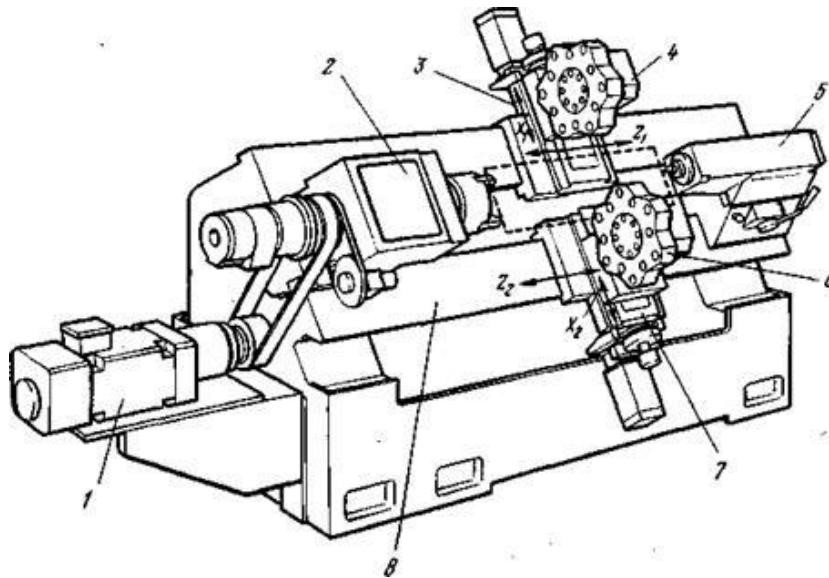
Компоновка токарного верстата з проти шпинделем [2]
